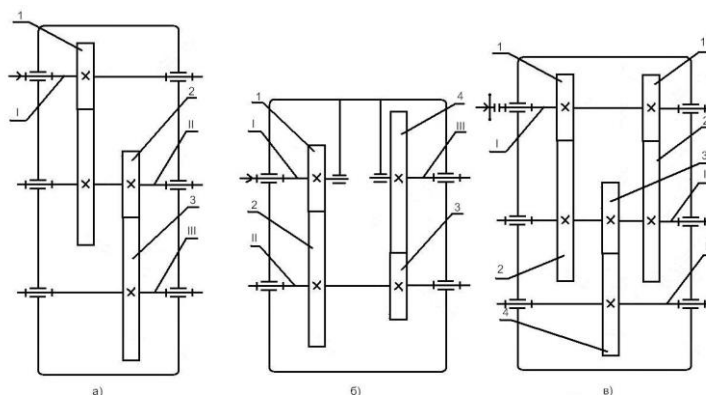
Кінематичні схеми двоступеневих зубчатих механізмів:
